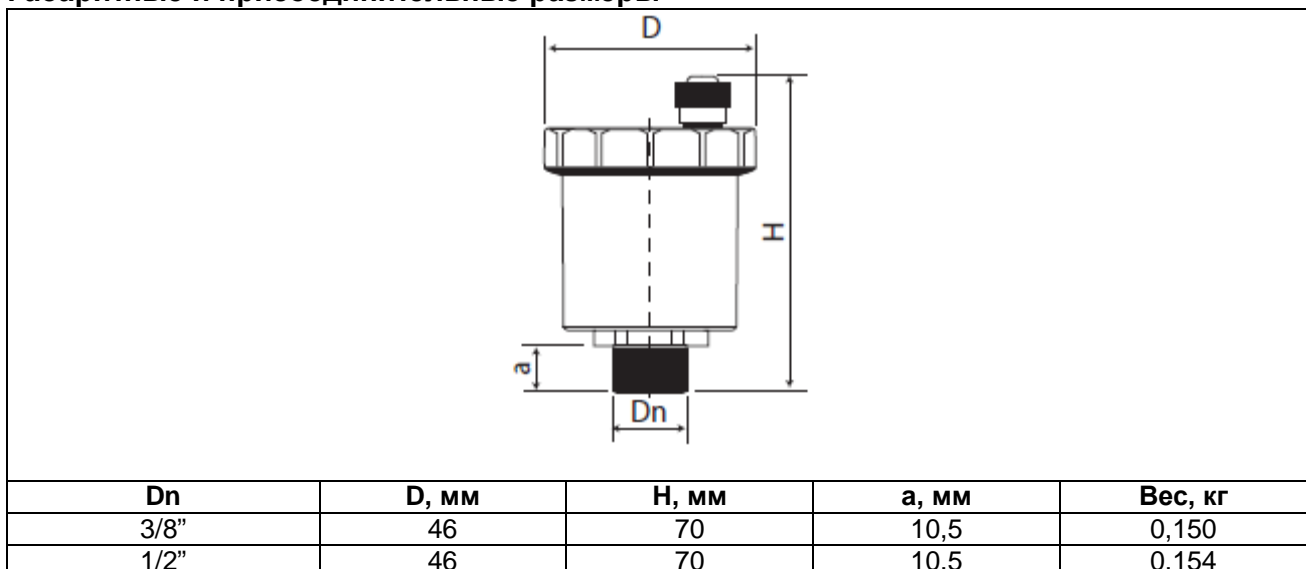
Габаритные и присоединительные размеры воздухоотводчика автоматического
